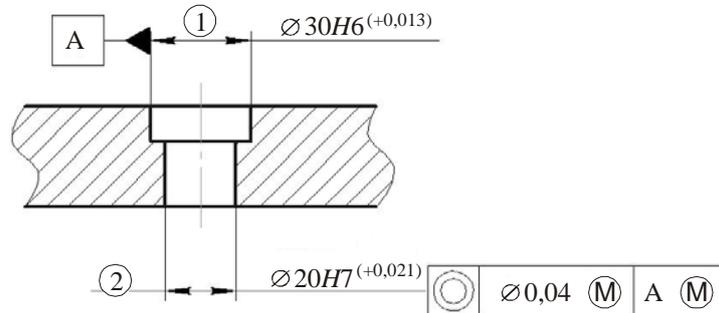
Фрагмент детали с базовой измерительной поверхностью
